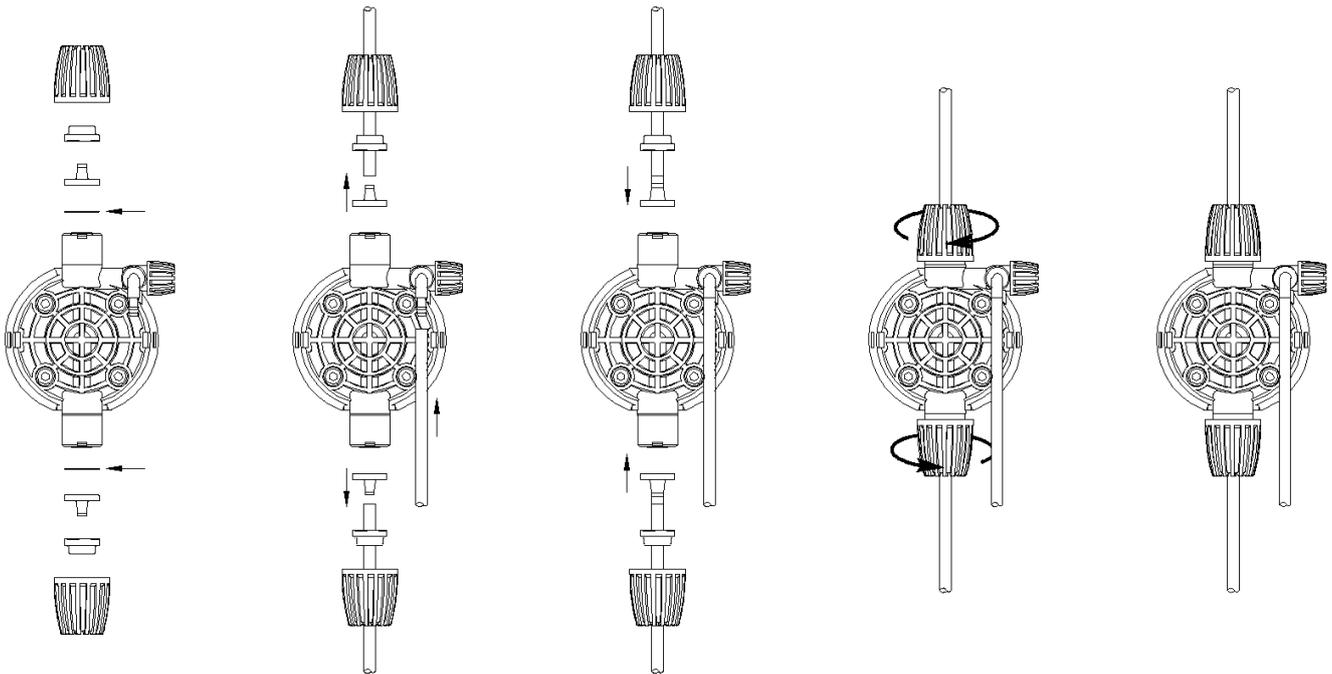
COLLEGAMENTI TUBI SUL CORPO POMPA – PUMP HEAD CONNECTIONS – SCHÉMA DE MONTAGE CONNECTIONS EXTERNES – ESQUEMA DE MONTAJE CONNEXION ESTERNAS - ANSCHLÜSSE DER SCHLÄUCHE AM PUMPENKÖRPER - Подключение трубок всасывающей и напорнок к гидравлической головке насоса
